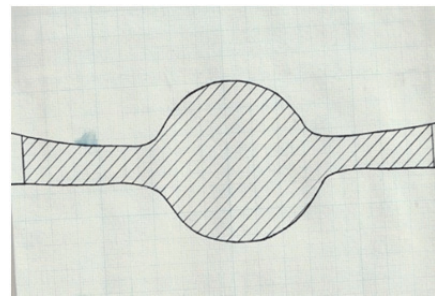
Контур поперечного сечения поковки после изготовления 2000 деталей, образец №10'
